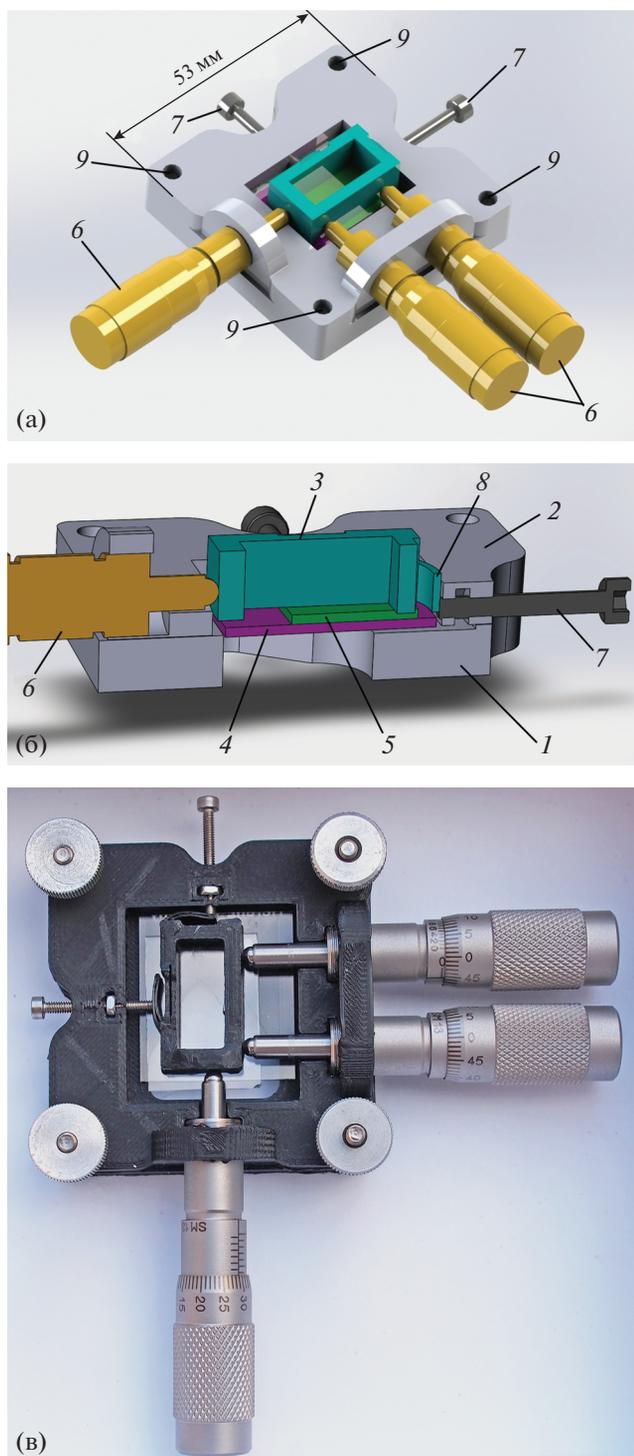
Устройство для совмещения микроструктур: а – общий вид 3D-модели, б – сечение, в – внешний вид модели. 1 – держатель нижней подложки; 2 – юстировочный узел; 3 – держатель верхней подложки; 4 – юстировочный узел; 5 – держатель верхней подложки; 6 – микрометрический винт; 7 – контрвинт; 8 – лепестковая пружина; 9 – отверстия под фиксирующие винты.
